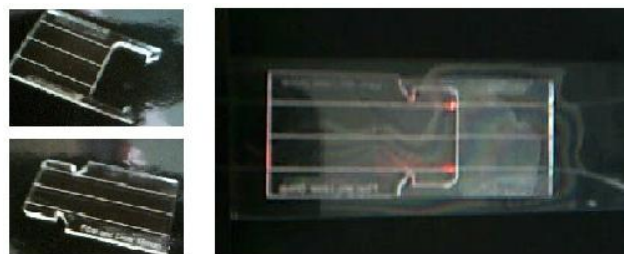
Acopladores de fibra manufacturados con láser [17].
